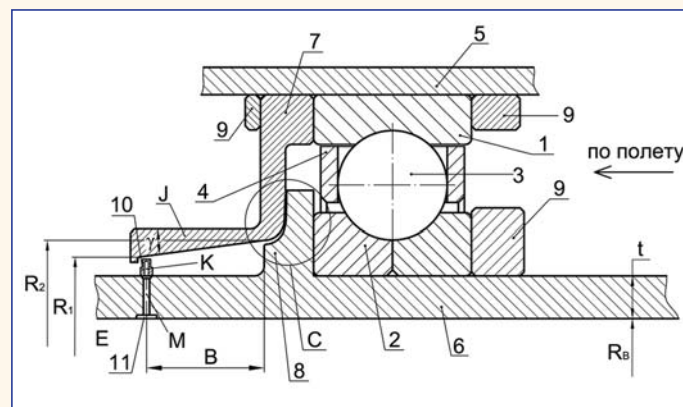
Опора ротора шарикового подшипника с гидродинамическим элементом
